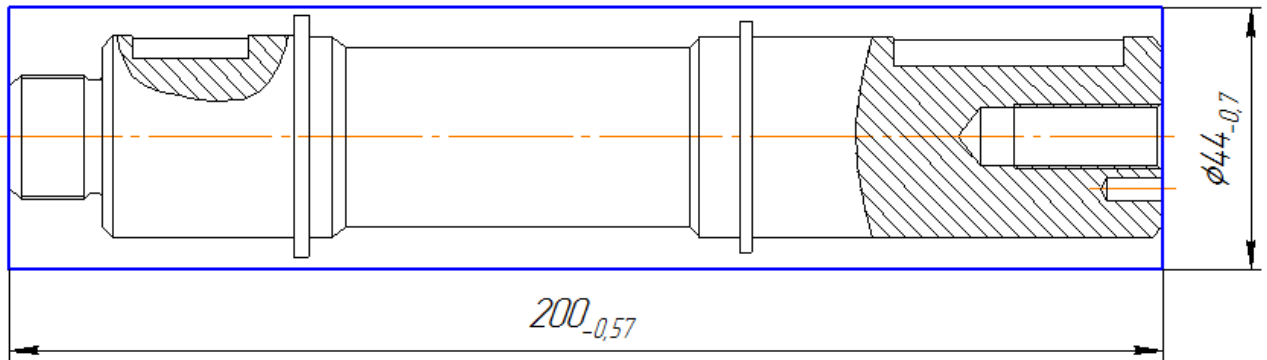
Ескіз заготовки отриманої з прокату розрізаного різцем
